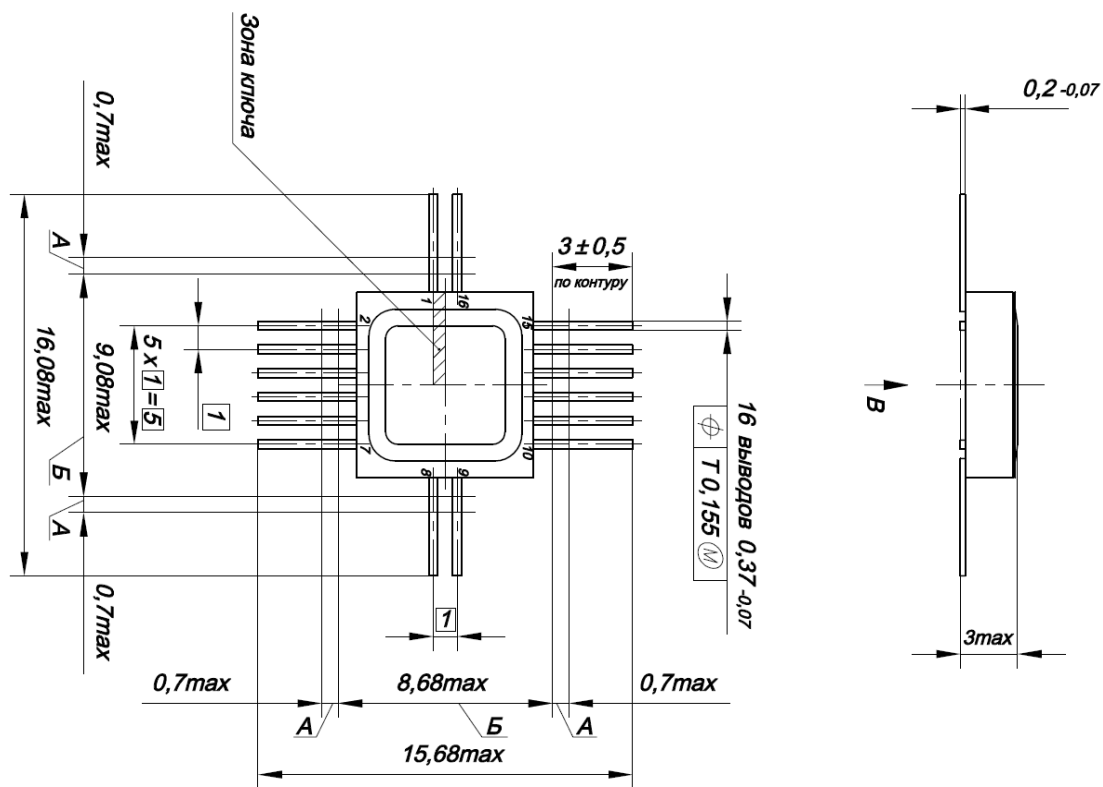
Габаритный чертеж корпуса Н04.16-1В
